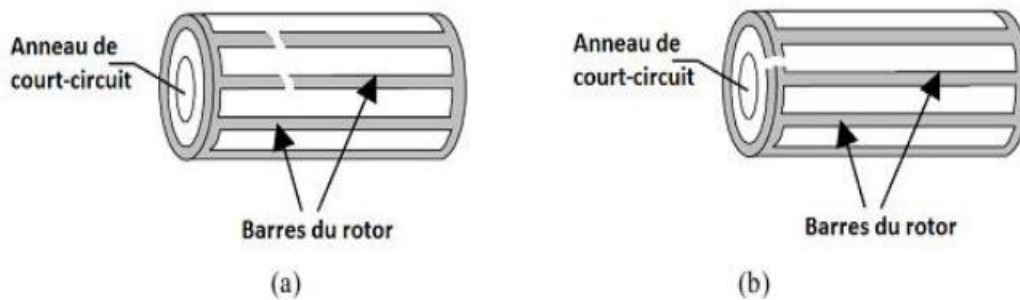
Défauts du rotor à cage : a) Rupture de barres ;
